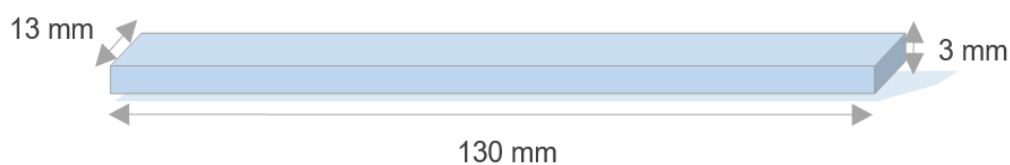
Dimensões dos corpos de prova ASTM D635 – 18.
